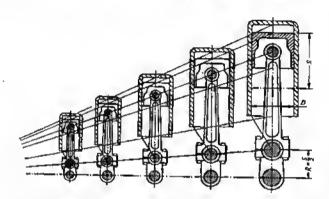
Serie somejante dimensional de los motores de combustión Interna
